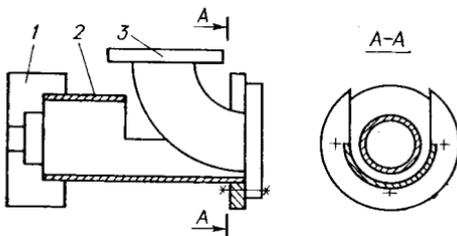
Приспособление для обработки сварных швов на отводах:
